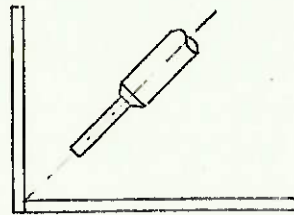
POSIÇÃO DO ELÉTRODO NA SOLDAGEM HORIZONTAL EM JUNTA DE CANTO
